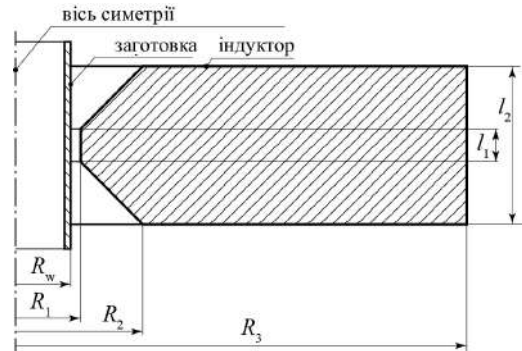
Поперечний переріз осесиметричного одновиткового індуктора із трубчастою заготовкою
